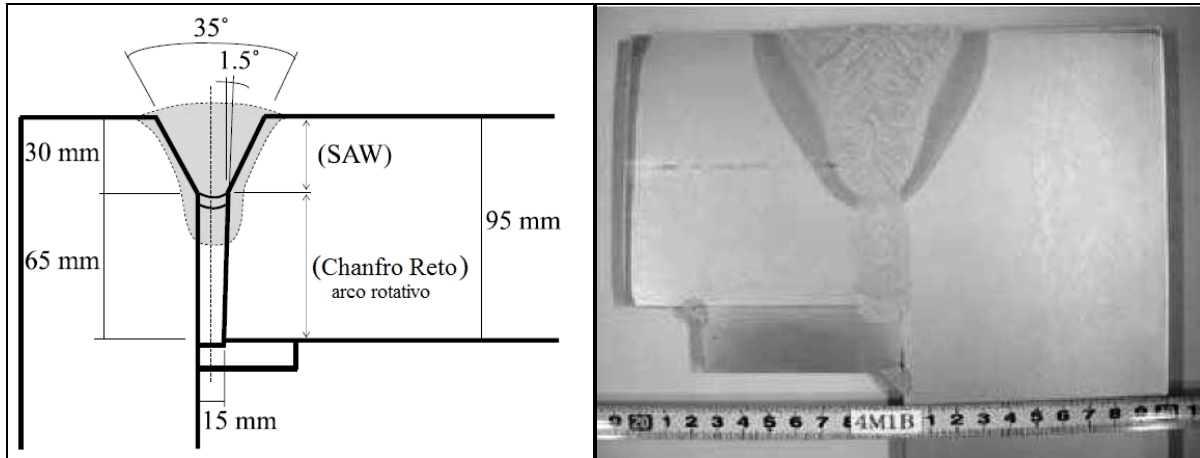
Soldagem GMAW-RE e SAW [17, adaptado]
